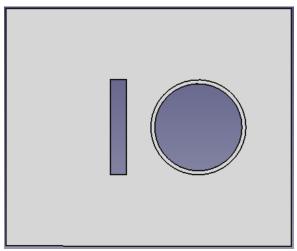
Maquette V1 - Pièce n°2 : Blower
